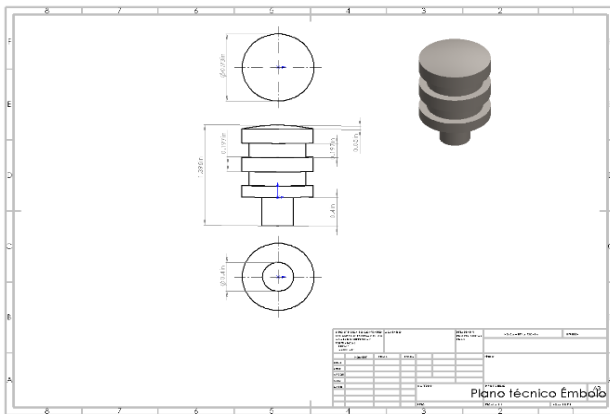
Ejemplo ilustrativo de Plano técnico para la manufactura del émbolo del actuador neumático
